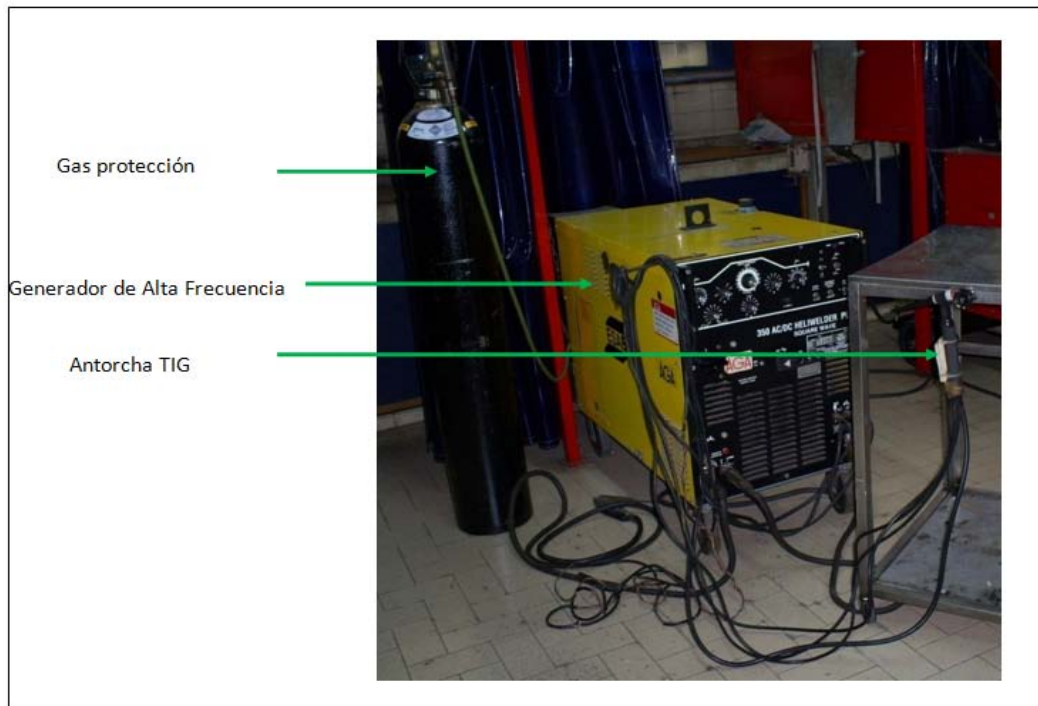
Equipo de soldadura GTAW.
